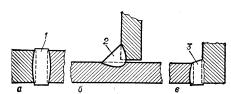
Виды сварных соединений и типы швов при электрошлаковой сварке: a — стыковое; δ — тавровое; e — угловое; f — стыковое шов; e — угловой шов; e — угловой шов; e — иов углового соединения.
